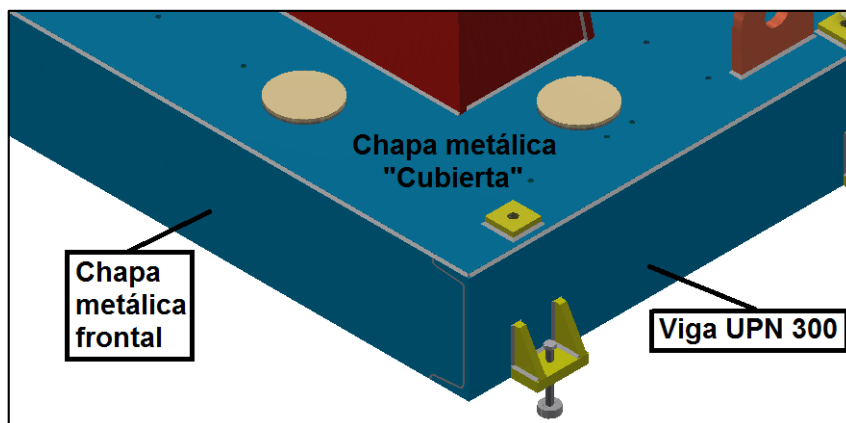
6 Detalle de la unión de la chapa metálica con las vigas UPN 300.
